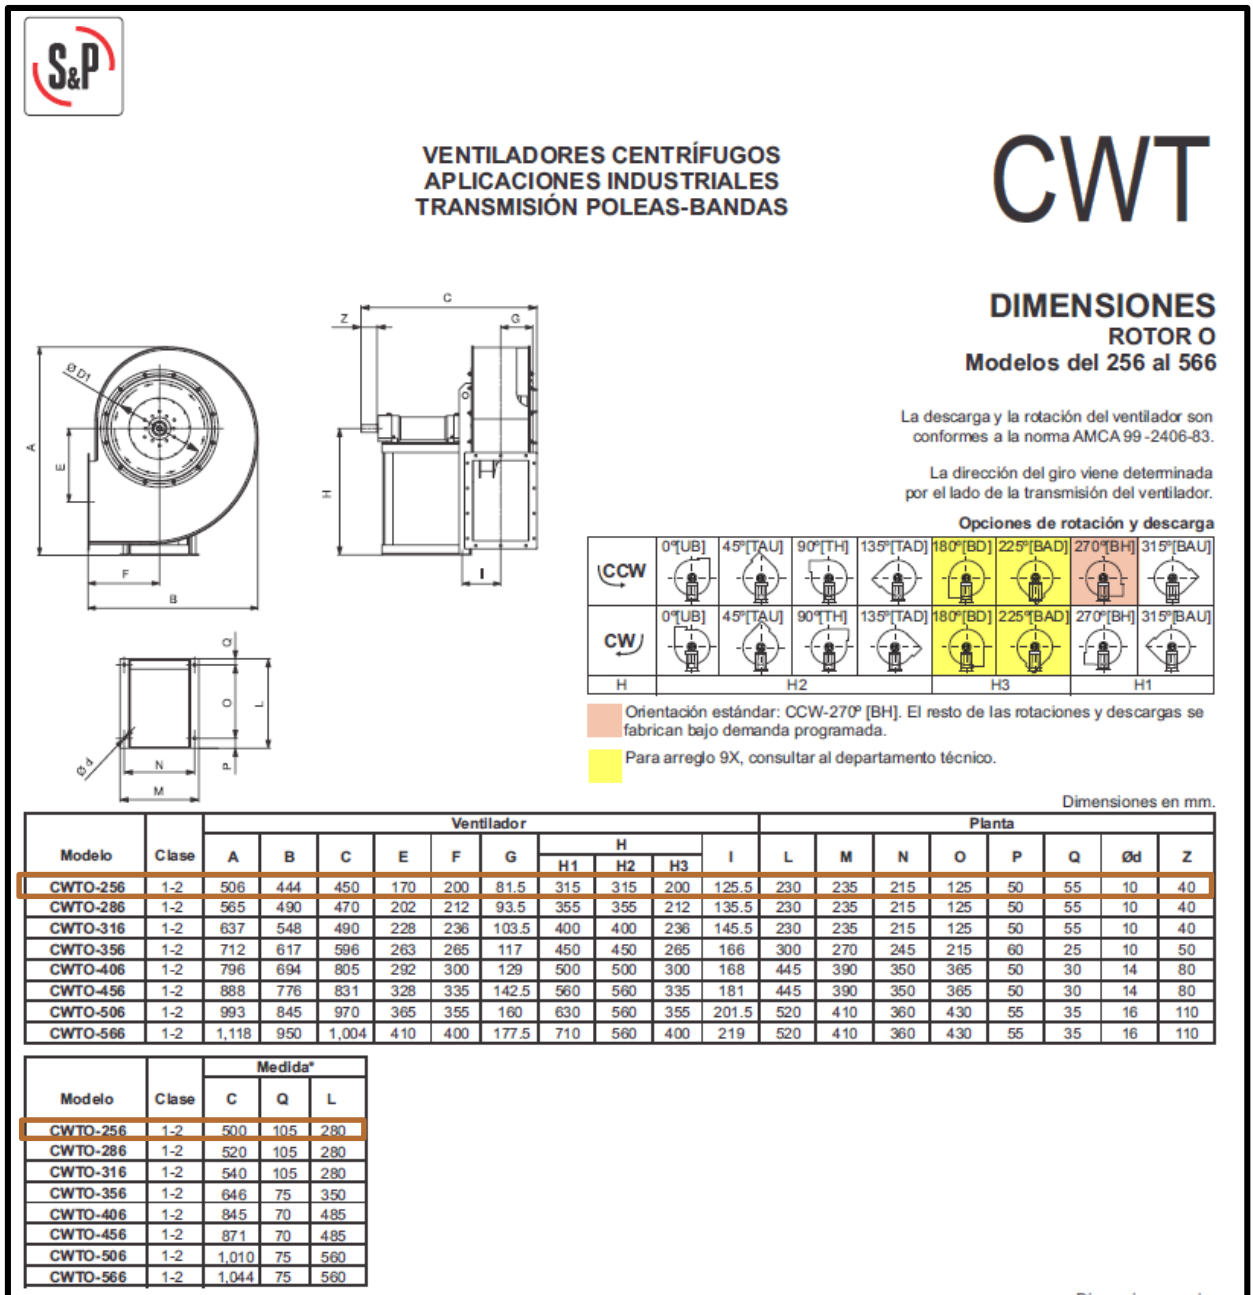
Dimensiones Ventiladores CWTO Rotor O
